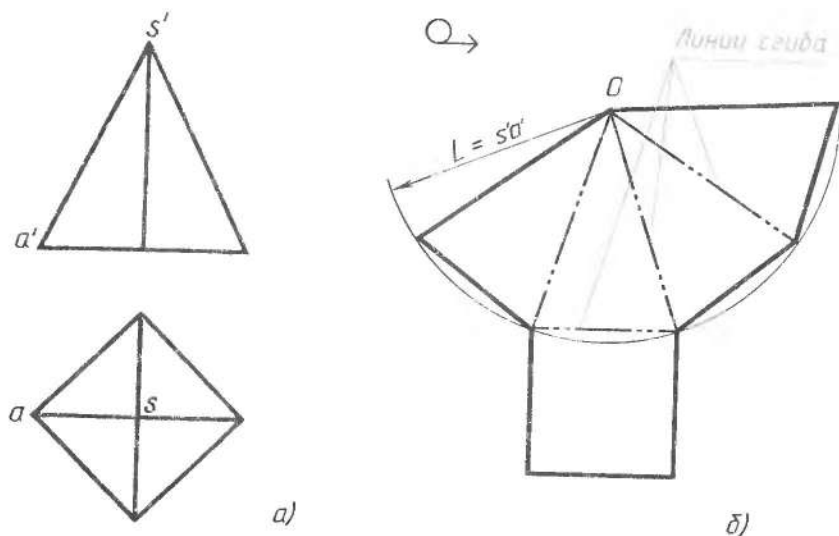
Построение чертежа развертки поверхностей пирамиды:
